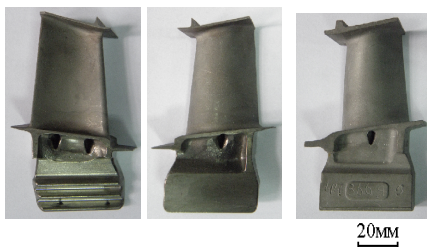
Робочі лопатки ТВТ до наземної установки типу Д-336 зі сплаву ЗМІ-ЗУМ2 (ЖС-32Е)
